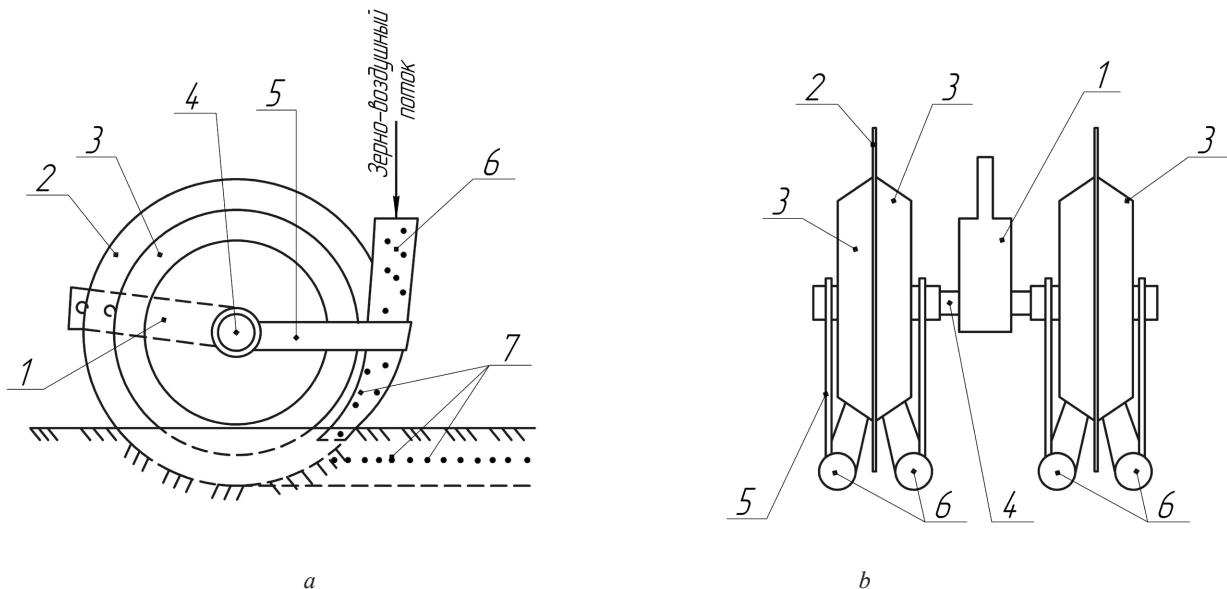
Технологическая схема работы двухдискового четырехстрочного сошника с усеченно-конусными ребордами и нулевым углом атаки дисков: *a* – вид сбоку; *b* – вид сверху; 1 – корпус; 2 – диск; 3 – реборда; 4 – ось; 5 – пластина; 6 – семя направитель; 7 – семена
